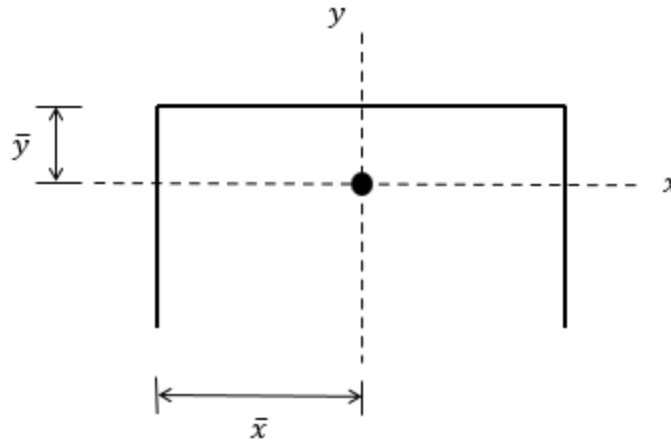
Ubicación del centroide de la soldadura.
